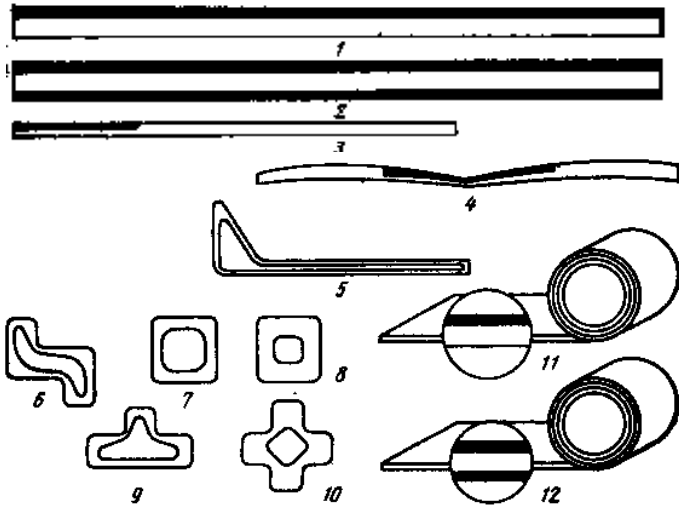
Поперечные сечения профилей сварных конструкций:
